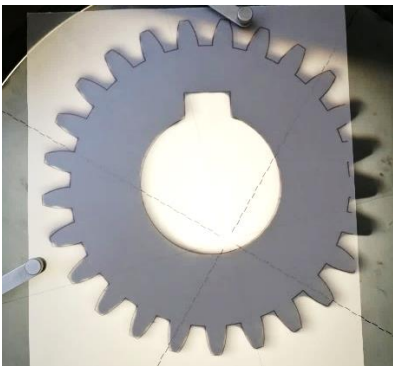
Proceso de medición chaveta, Fuente: El Autor
